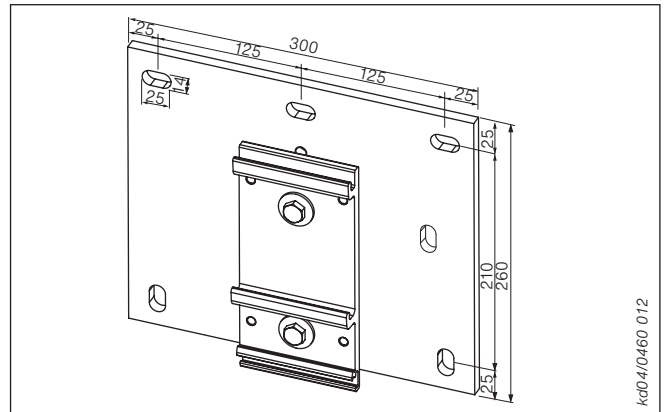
Consola tipo D – Fijación mural con placa de montaje grande
